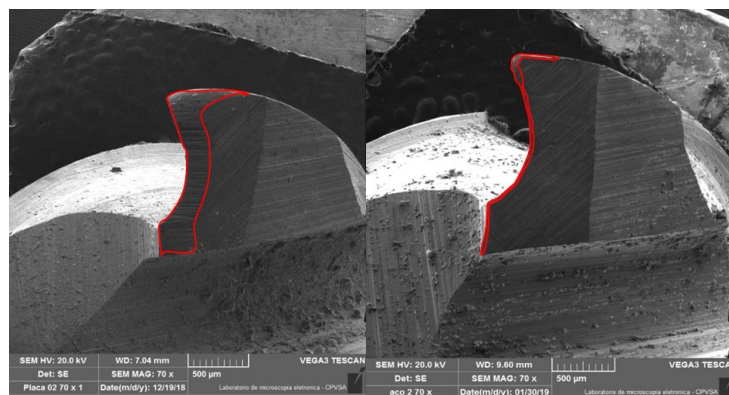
Desgaste de flanco na Fresa 2 (esquerda) e desgaste de flanco na Fresa 5 (direita).
